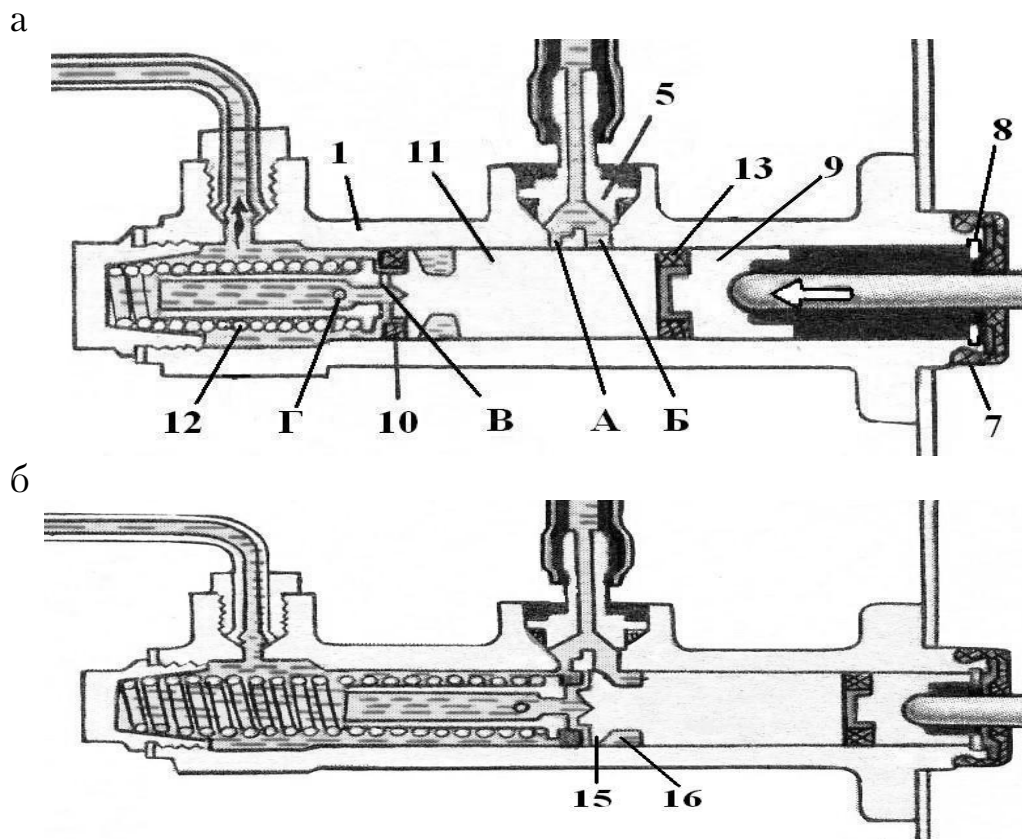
Схема работы главного цилиндра гидропривода выключения сцепления автомобилей ВАЗ:
